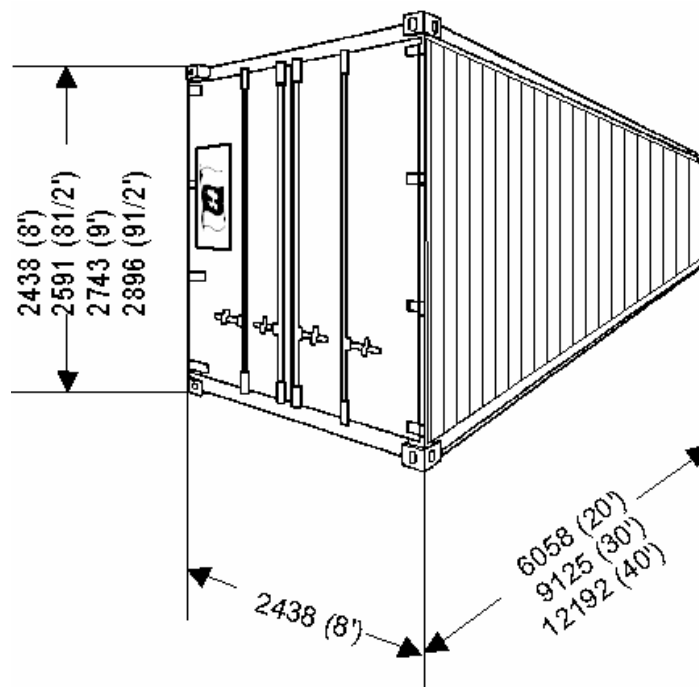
ISO-1 Standardcontainer in geschlossener Bauweise
